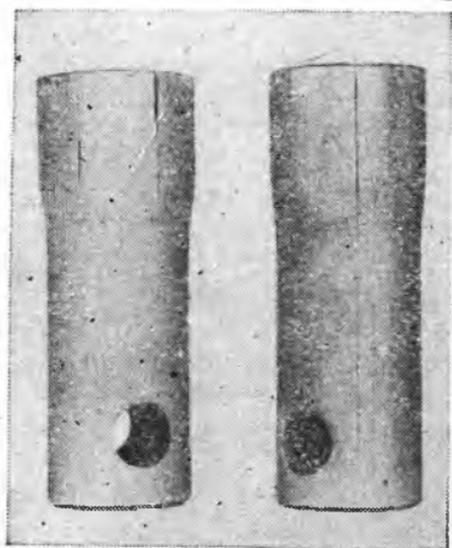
Волосовины на поверхности заготовок торцовых ключей
